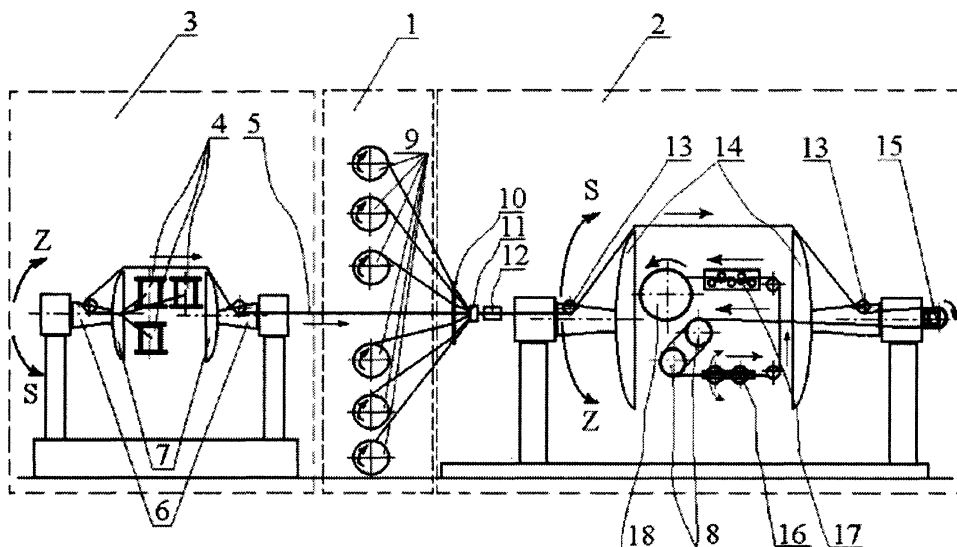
Схема изготовления двухслойного витого проволочного изделия
